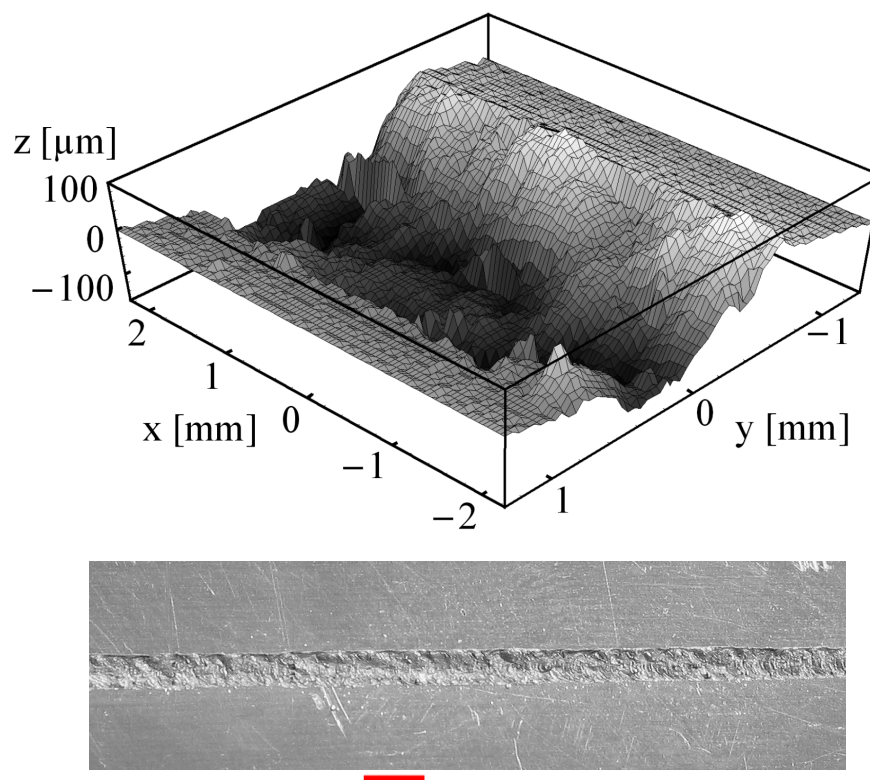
Oben: Ausschnitt der Oberflächen-Topologie einer Laserschweißnaht. Die Oberfläche wurde mittels eines Laserprofilometers abgerastert. Die Variationen in der Nahtoberfläche betragen $165\ \mu\text{m}$. Unten: Photographie dieser Schweißnahtprobe. Es sind $5\ \text{cm}$ der Naht dargestellt (Darstellung im Verhältnis 2:1 zum Original); der rote Balken (entspricht $4.5\ \text{mm}$) markiert in x -Richtung den in 3D gezeigten Ausschnitt. Siehe auch [87].
